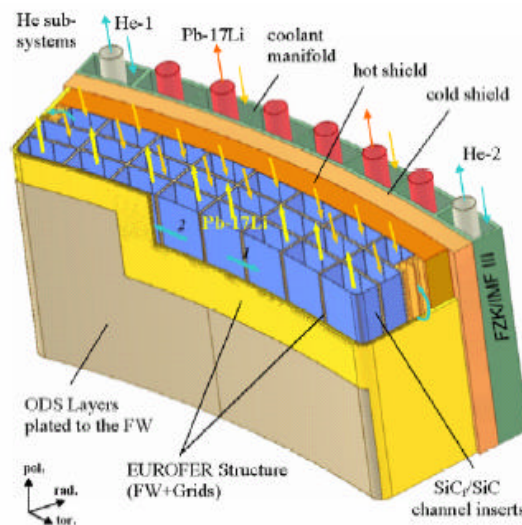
Vista Isométrica de un módulo del “dual-coolant blanket”. Ref. 79.
